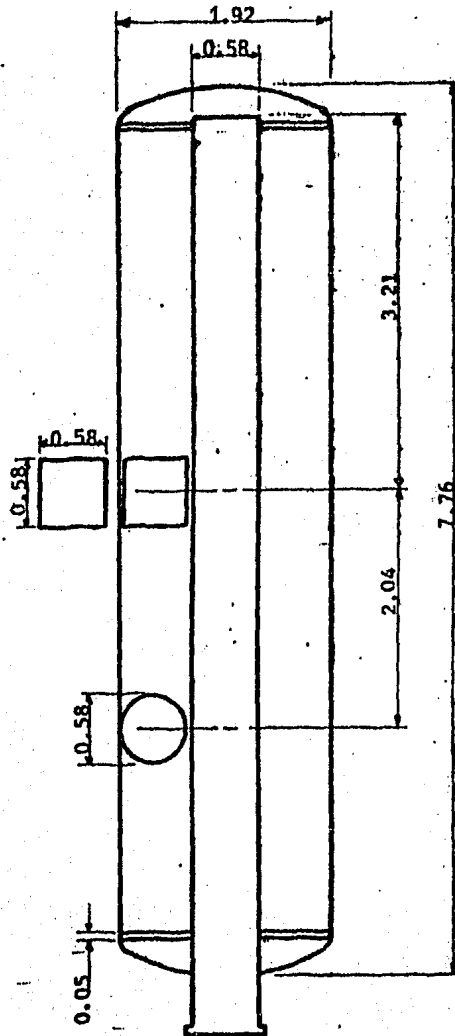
Esquema del arreglo de separadores de baja presión en la Planta de Evaporación.
